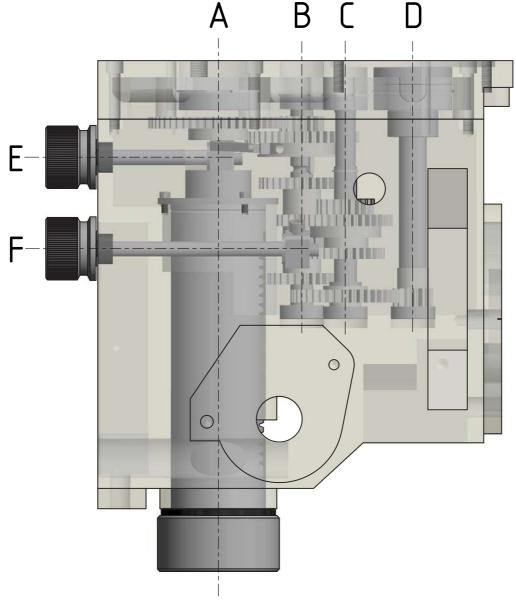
Fräskopf 1 von 6 - Milling head 1 von 6
